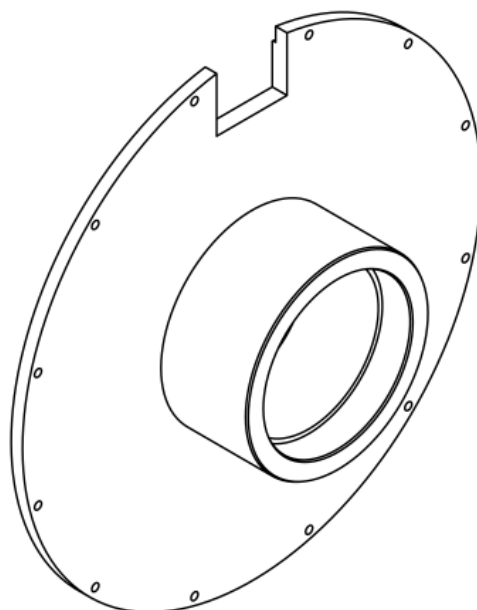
Flange External Frontal e Posterior Gerador da Bancada
